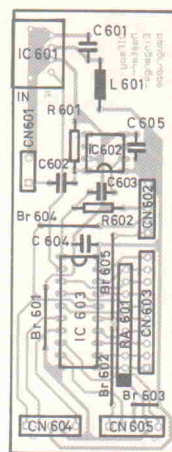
Bestückungsplan der Master-Eingangsbaugruppe.
